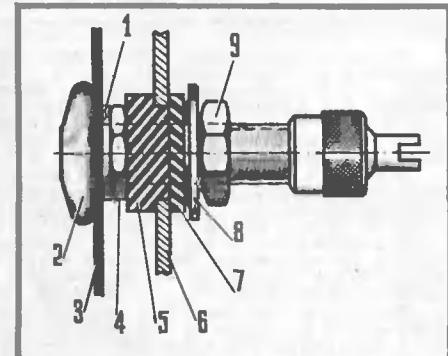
1 — текстиловая шайба; 2 — вентиль; 3 — камера; 4 — внутренняя гайка; 5 — уплотнительная втулка; 6 — обод колеса; 7 — резиновая шайба; 8 — стальная шайба; 9 — гайка.
